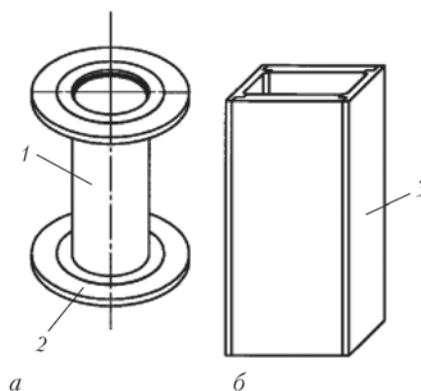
Конструкции кристаллизаторов, изготовленных ковкой из слитков: а — кованый бесшовный (1) с приваренным фланцем (2); б — состоящий из четырех отдельных листов (3)
